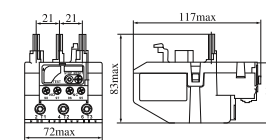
configuração geral da TRR2-93 e dimensão da instalação
